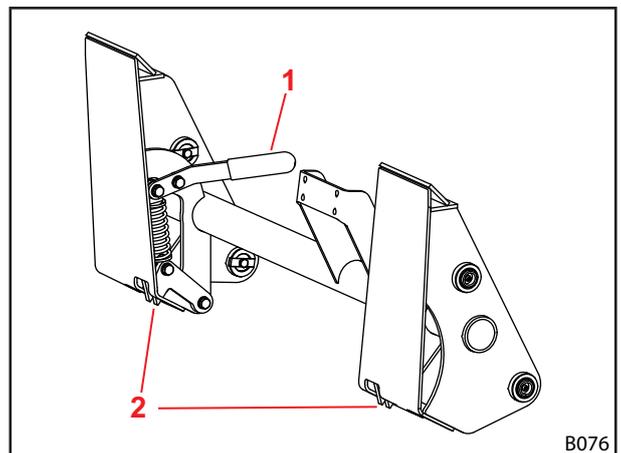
Werkzeug-Verriegelung am Skid-Steer-Wechselrahmen
